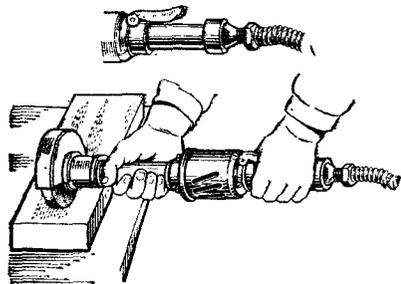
Прием шлифования поверхностей пневматической шлифовальной машинкой
